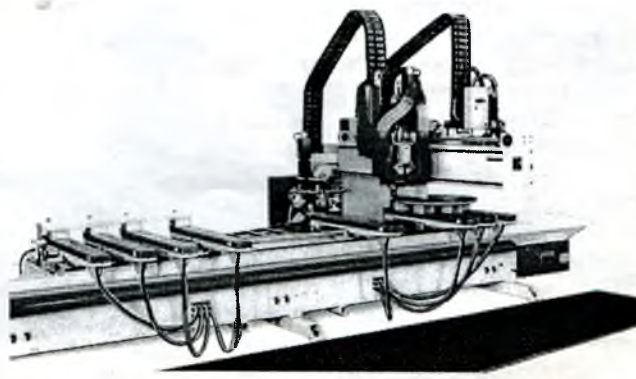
Обрабатывающий центр BIMA 610 для фрезерования, сверления и окантовки кромок
